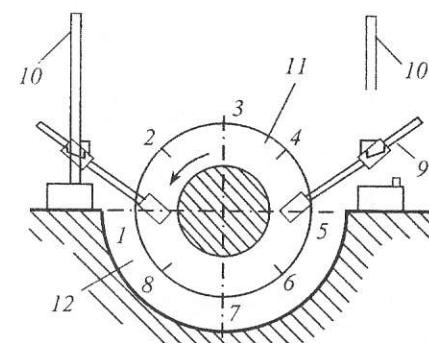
Схема вимірювання биття упорного диска двома індикаторами:
